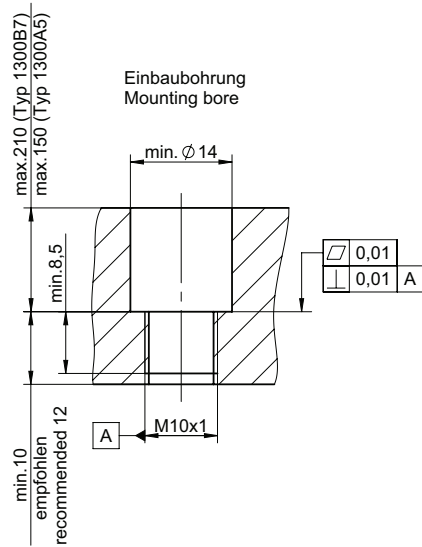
Einbaubohrung bei brennraumbündiger Montage
